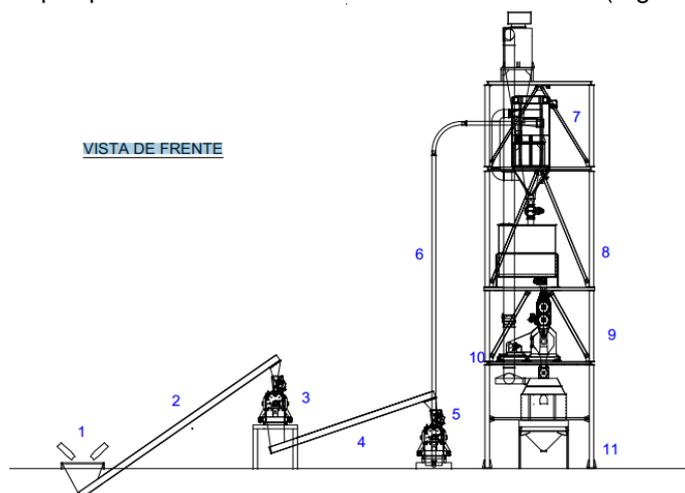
Esquema de la disposición de maquinaria en una planta de pelletizado tradicional.
